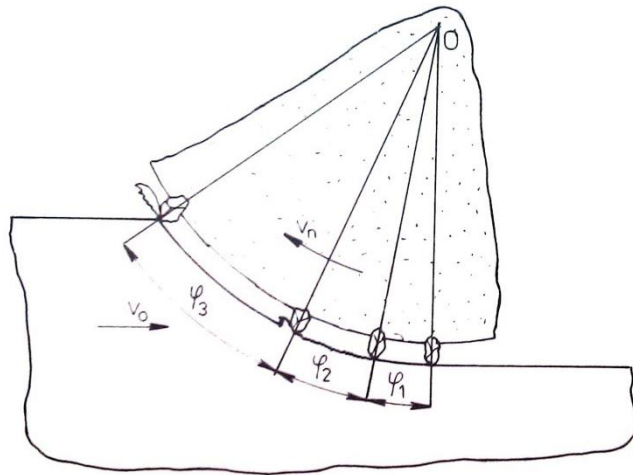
Brúsny nástroj a geometria brusných zrn [9]
